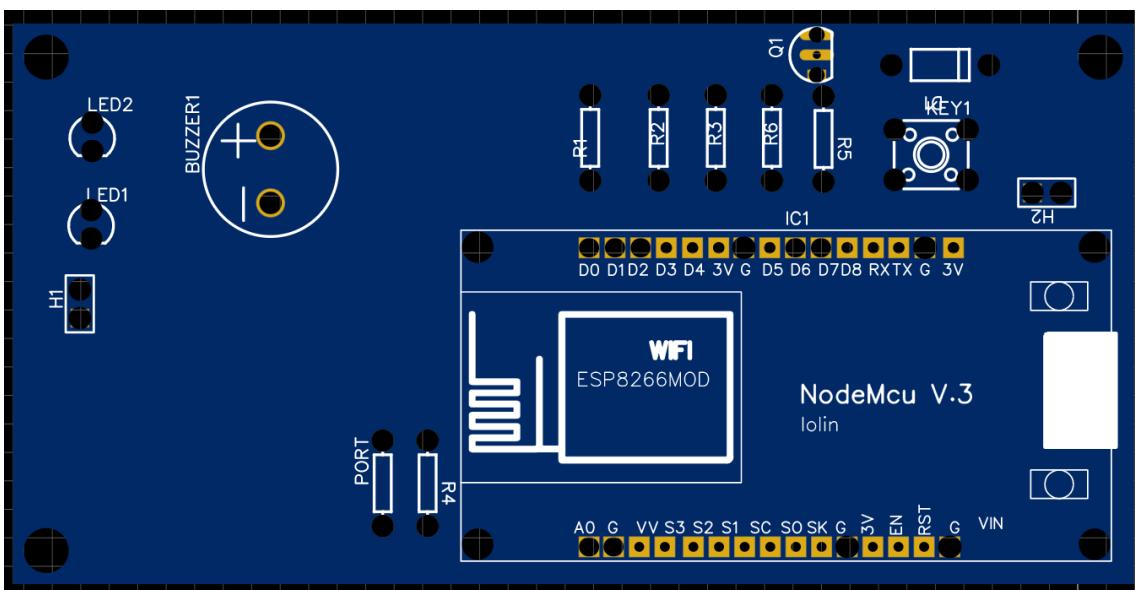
PCB Üç Boyutlu Modeli (Komponentler Üzerinde)
